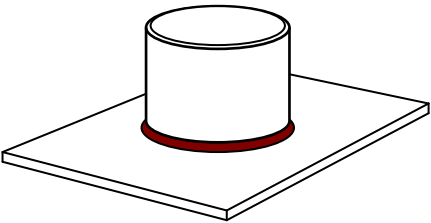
Posición del ensamble para la realización de la soldadura sobre cabeza.
